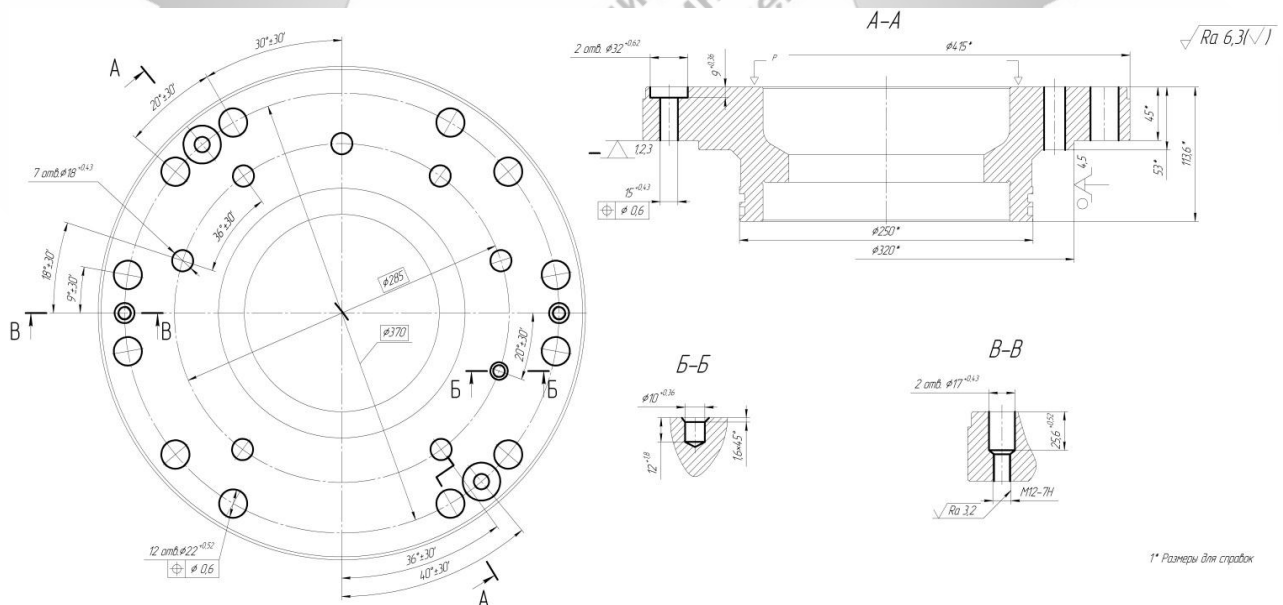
Операційний ескіз обробки для операції 045
